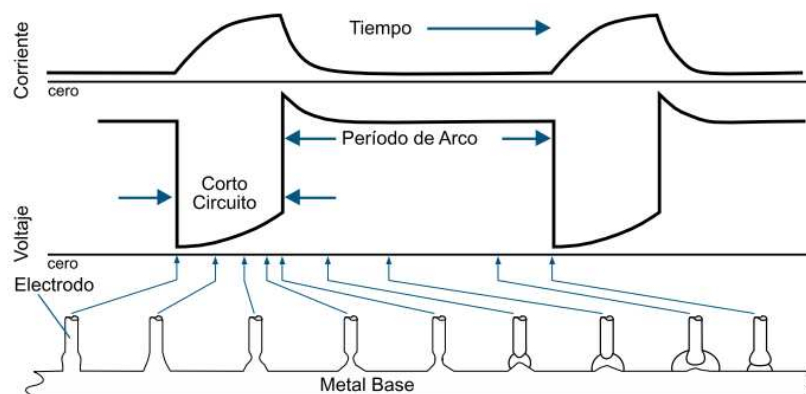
Voltaje y corriente de soldadura para un ciclo por corto circuito
